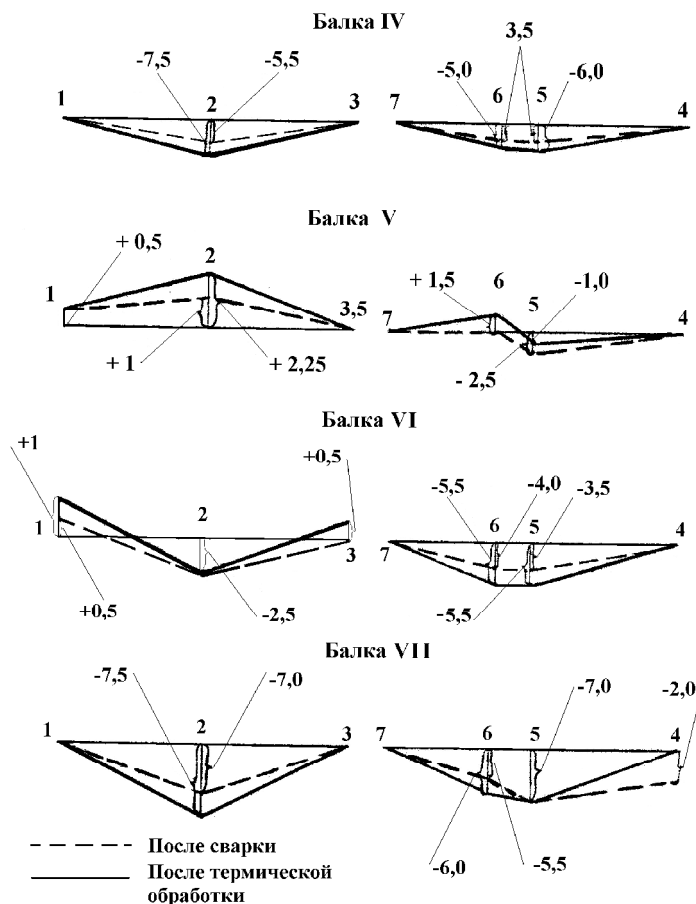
Схема измерения величины прогиба в балках IV–VII после сварки и термической обработки
